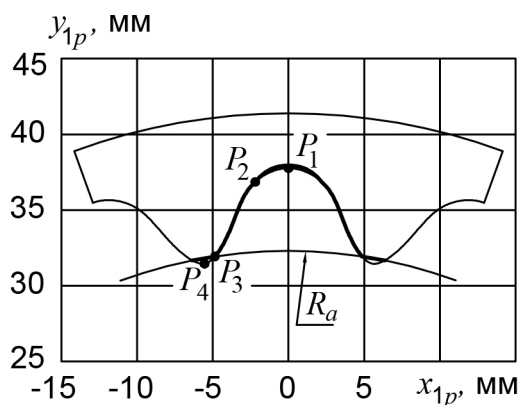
Формирование вершин и впадин зубьев жесткого колеса
